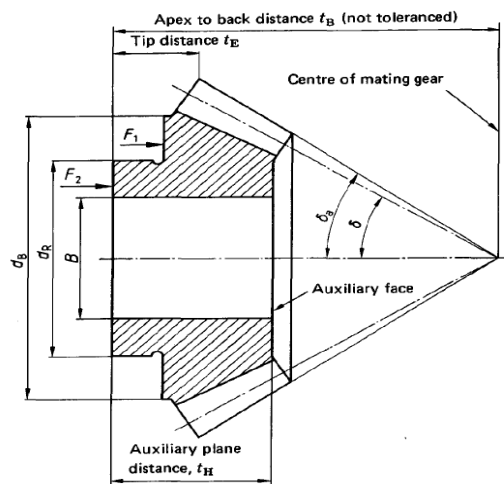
Principales dimensiones de la pieza en su fase de torneado [8]
